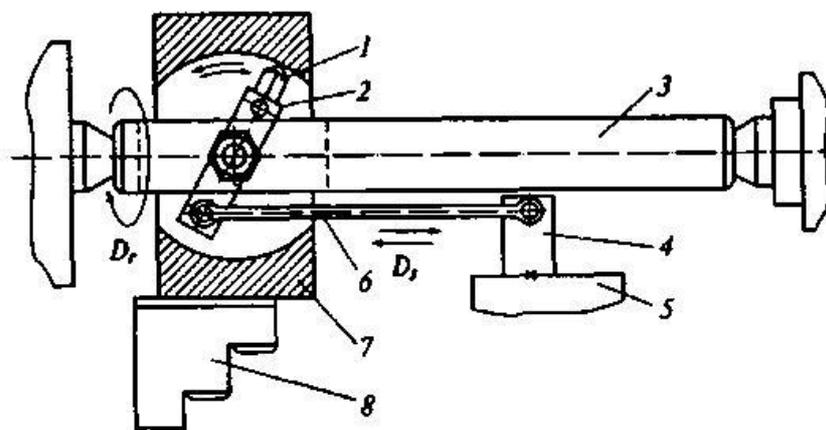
Приспособление для растачивания сферических поверхностей 1 — резец; 2 — державка; 3 — оправка; 4 — колодка; 5 — суппорт; 6 — тяга; 7- заготовка; 8 — трехкулачковый патрон
